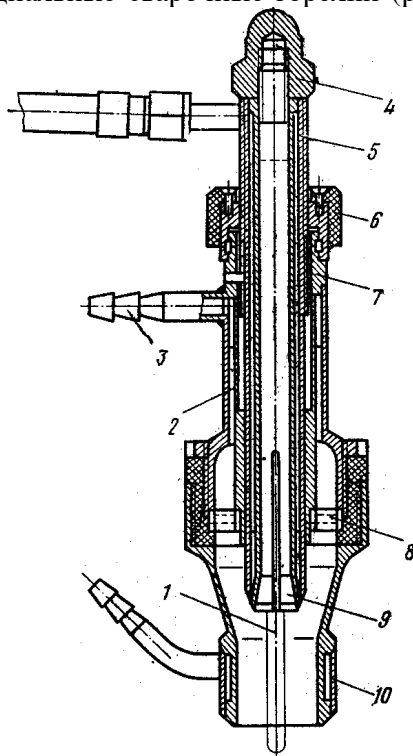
Схема горелки для автоматической сварки вольфрамовым электродом:
